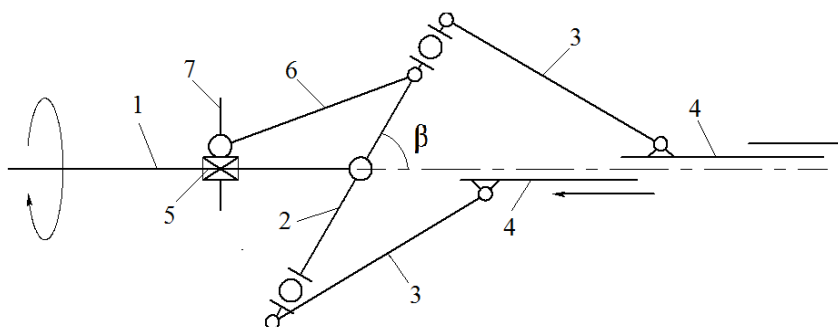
Механизм качающейся шайбы для работы с двумя ножами
